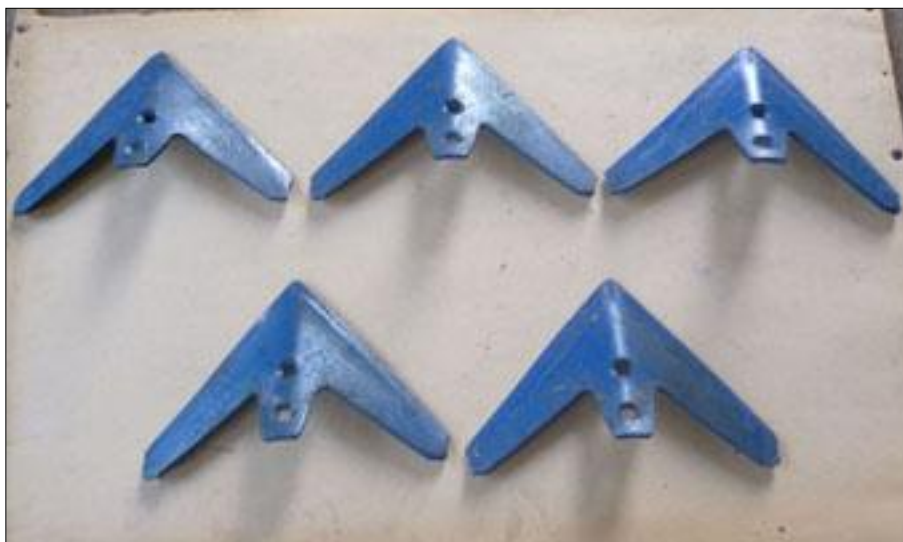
Стрельчатые лапы 043.052.007 наплавленные фирмы «Велес»,
